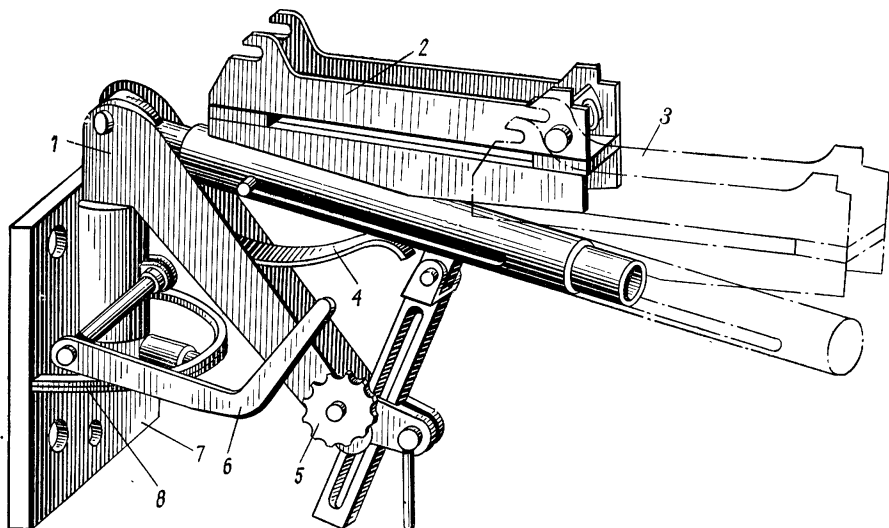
Пулеметный станок СПН; масса 12 кг:
